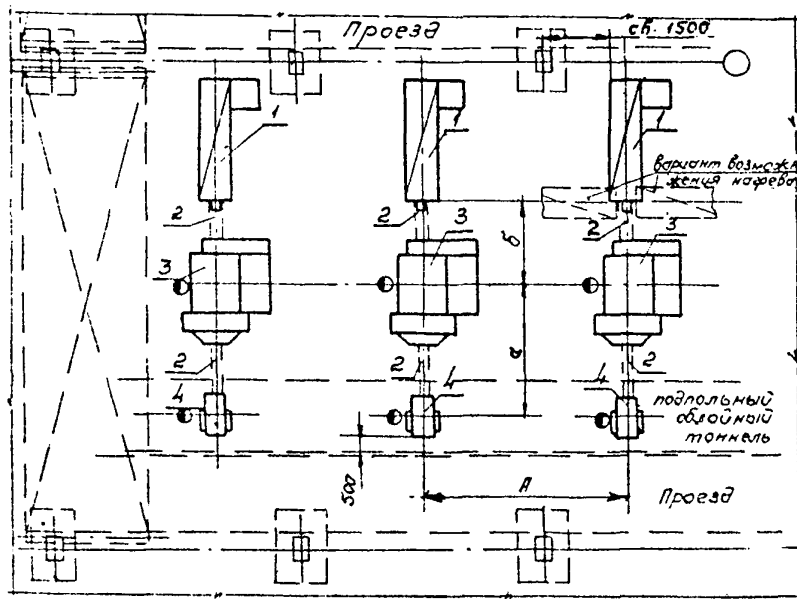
Схема штамповочных линий при поперечном расположении их в пролете на базе КМШ с продольным расположением коленчатого вала: 1 - индукционный нагреватель; 2 - транспортер; 3 - кривошипный горячештамповочный пресс; 4 - обрезной пресс
